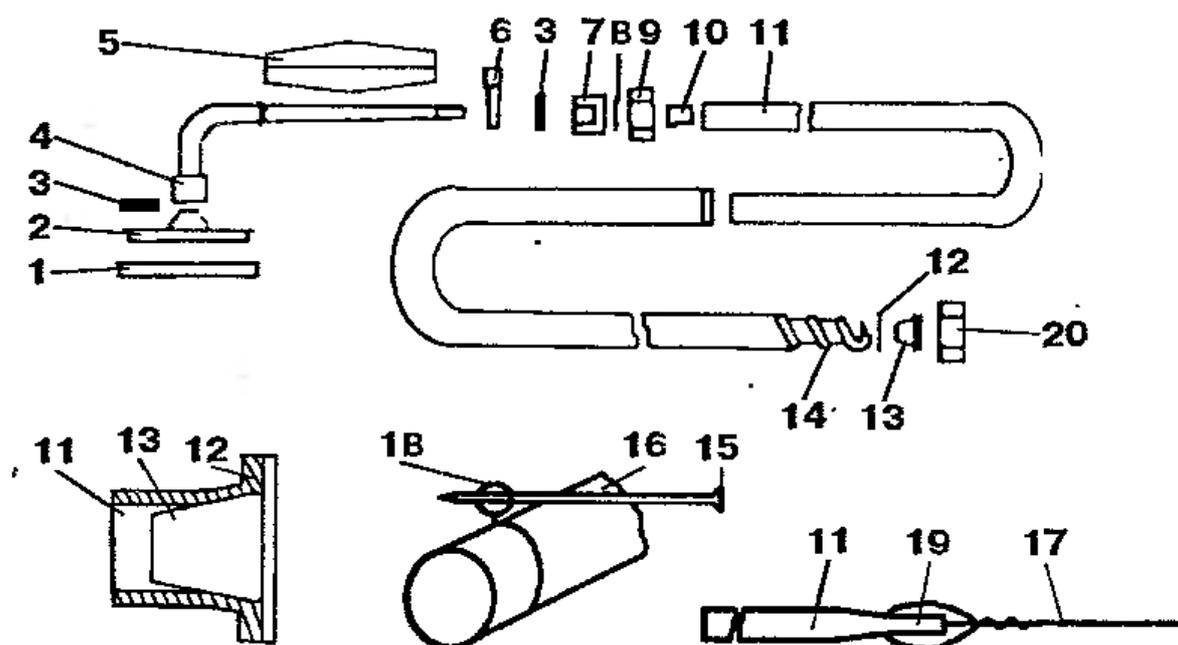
Гибкий резиновый шланг с душевой сеткой: 1 — резиновое кольцо; 2 — душевая сетка; 3 — уплотнение; 4 — остов; 5 — рукоятка; 6 — петля; 7 — специальная гайка; 8 — резиновая прокладка; 9, 15 — накидная гайка; 10 — латунный ниппель; 11 — резиновая трубка; 12 — пластмассовая или латунная шайба; 13 — пластмассовый ниппель; 14 — хромированная латунная спиральная оболочка
